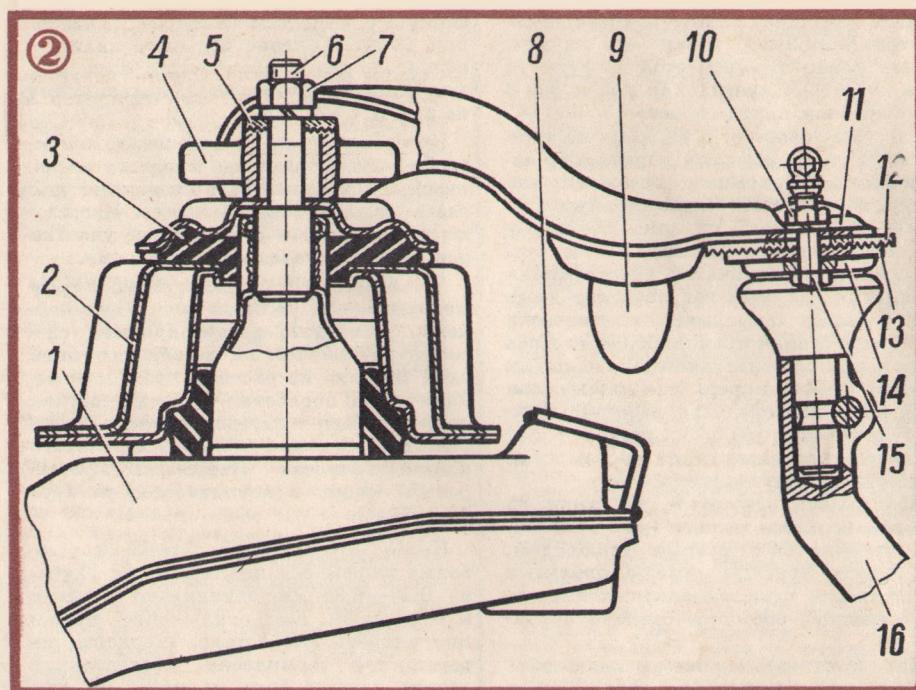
Установка верхнего рычага с измененным креплением оси и шарового шарнира: 1 — поперечина; 2 — лонжерон рамы; 3 — верхняя подушка; 4 — ось верхнего рычага; 5 — зубчатая накладка; 6 — шпилька поперечины; 7 — гайка; 8 — угольник; 9 — буфер отбоя; 10 — гайка крепления; 11 — верхний рычаг; 12 — зубчатая пластина, приваренная к рычагу; 13 — зубчатая пластина шарового шарнира; 14 — шаровой шарнир; 15 — стяжной болт; 16 — поворотная стойка.
